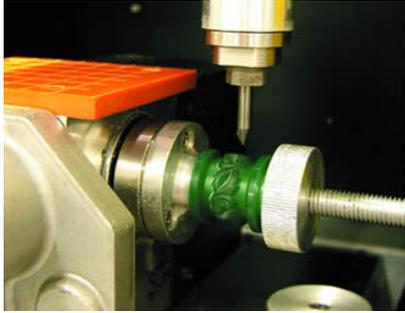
Máquina CNC de três eixos usinando um anel.
